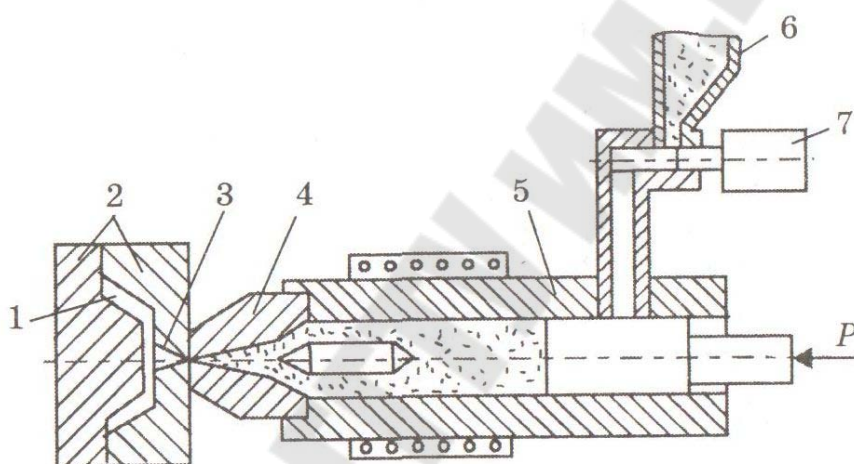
Схема изготовления детали из термопласта литьем под давлением
